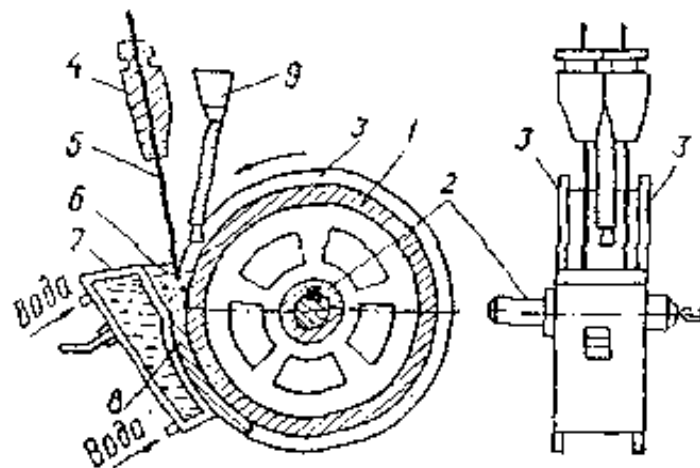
Схема установки ОКС-7755 для автоматичного електрошлакового наплавлення:
